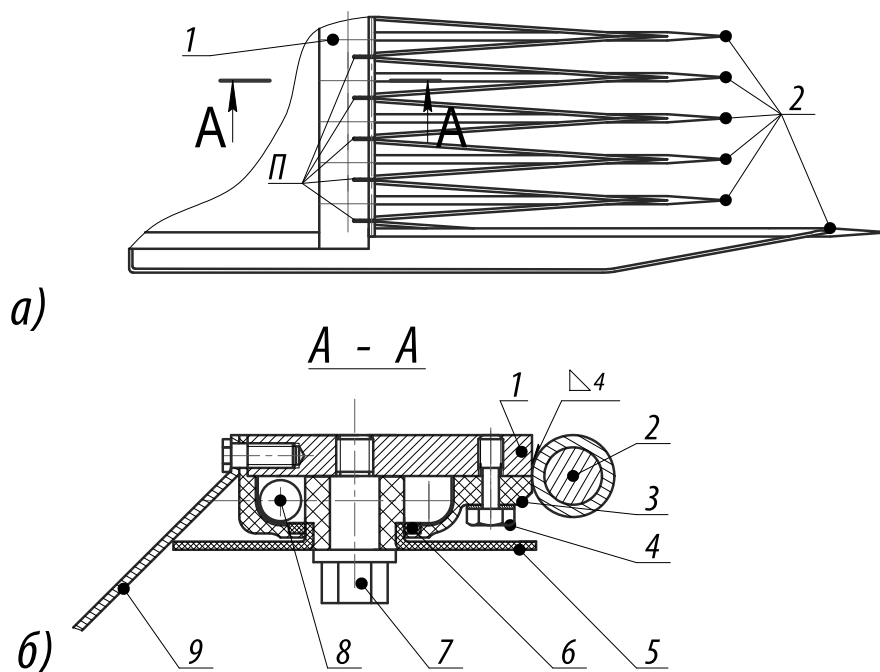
Схема жатки с режущими устройствами, оснащёнными абразивными дисками: а) фрагмент жатки (без мотовила), вид сверху; б) сечение А – А: 1 – брус; 2 – делитель; 3 – кожух; 4 – болт; 5 – абразивный диск; 6 – уплотнение; 7 – ось; 8 – крыльчатка; 9 – задняя стенка; П – прорези в брусе
